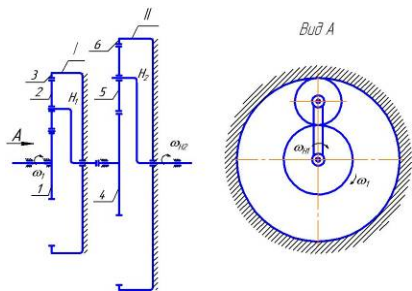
Схема планетарного двухступенчатого редуктора типа CPU-22: 1 -вал шестерни I ступени редуктора; 2,5 - сателлиты ступеней; 4 - солнечная шестерня II ступени; 3,6 - зубчатые венцы ступеней; H_1, H_2 - водило; $\omega_1 = \omega_6$ - угловая частота вращения быстроходного вала редуктора; $\omega_{H_2} = \omega_T$ - угловая частота вращения тихоходного вала редуктора (угловая частота вращения мельницы)
